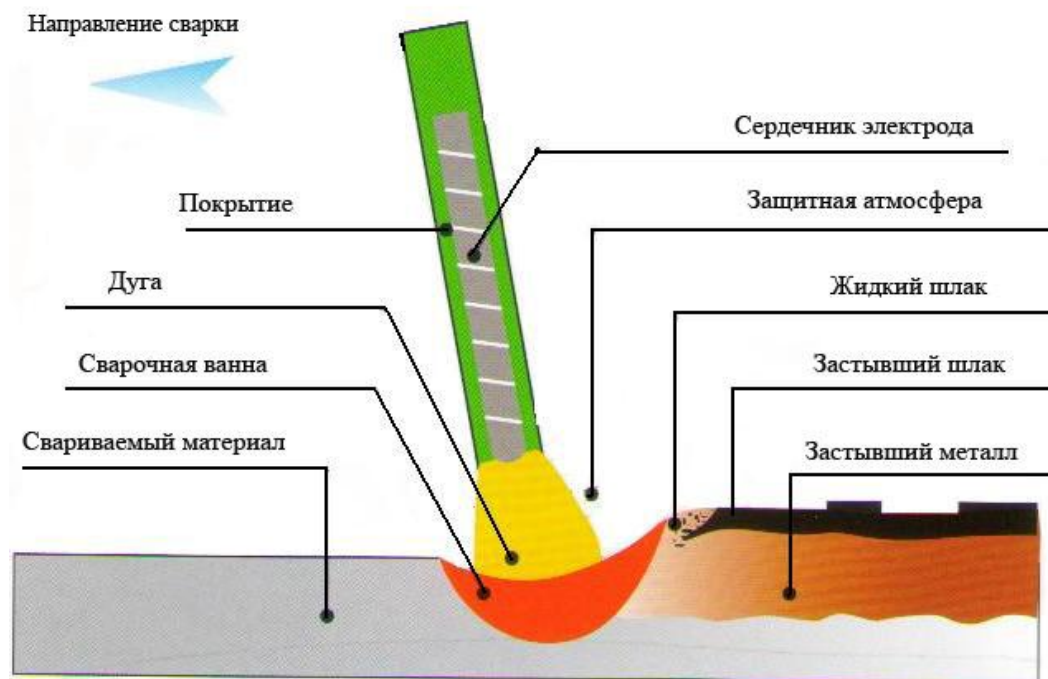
Схема ручной дуговой сварки
